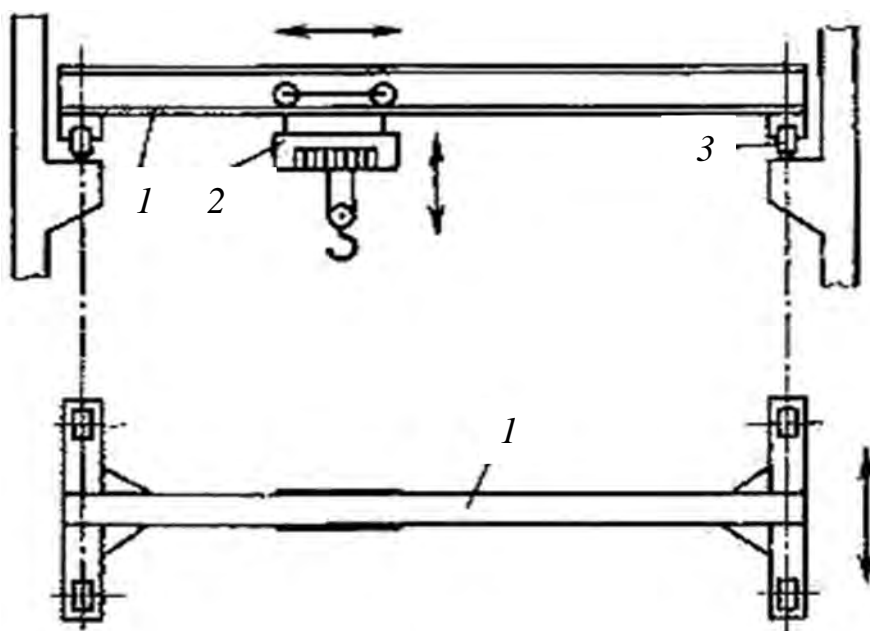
Схема опорной кран-балки: *1* – главная балка; *2* – механизм подъема и перемещения; *3* – концевые балки
